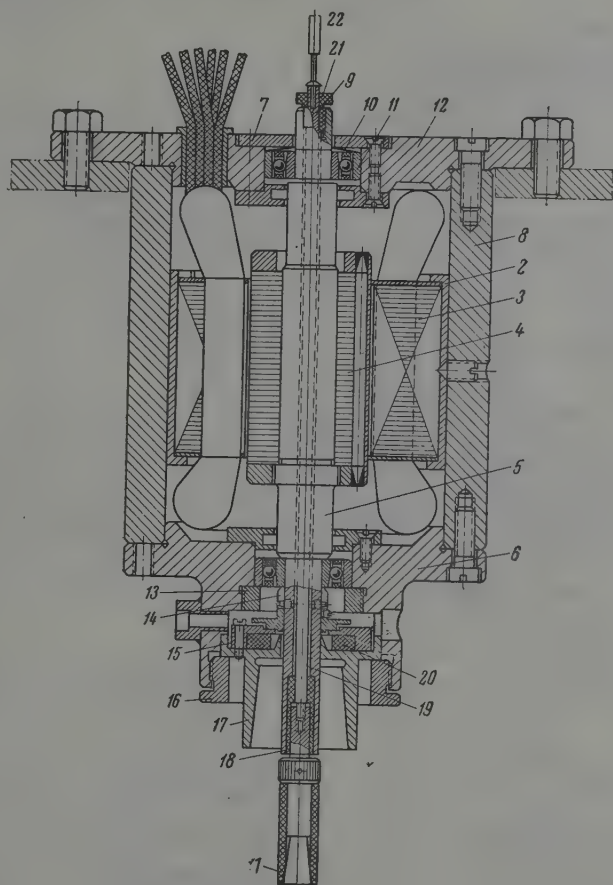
Высокочастотный электродвигатель: 1 — электрод; 2 — стакан статора; 3 — пластина статора; 4 — пластина ротора; 5 — вал ротора; 6 — щиток нижний; 7 — шайба; 8 — корпус; 9 — валик; 10 — пружина; 11 — подшипник; 12 — щиток верхний; 13 — гайка; 14 — втулка; 15 — меднографитное кольцо; 16 — гайка; 17 — конус; 18 — изолирующая втулка; 19 — изолирующая трубка; 20 — упругий элемент; 21 — изолирующая втулка; 22 — меднографитная игла
